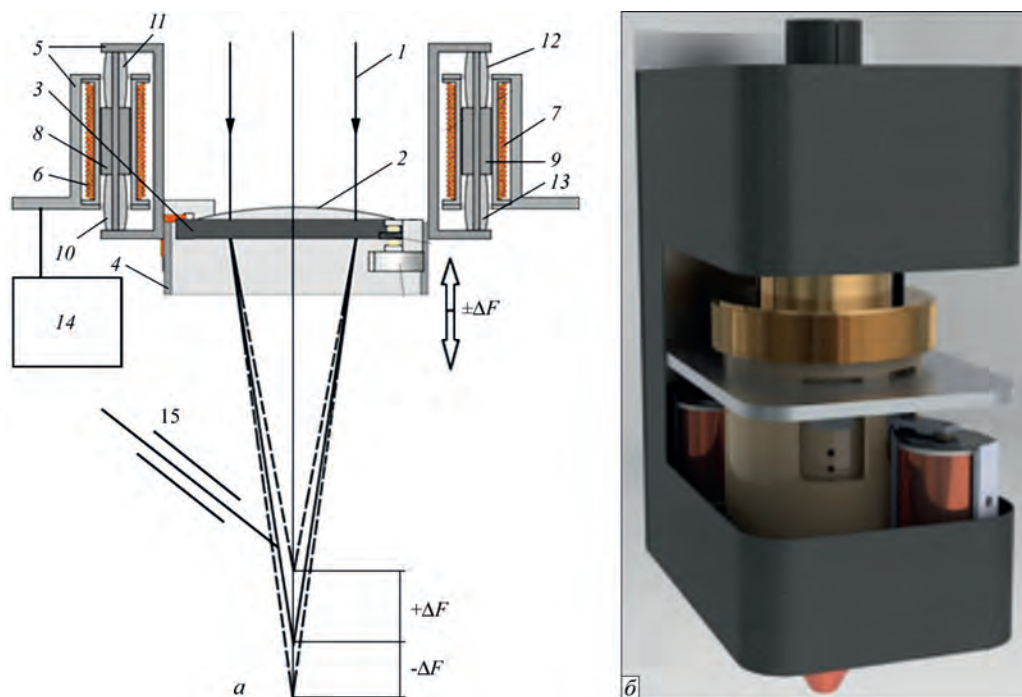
Схема конструкции (а) и общий вид (б) головки для лазерной и гибридной лазер-MIG сварки с системой возвратно-поступательного перемещения (сканирования) фокуса ($\pm\Delta F$) вдоль оси излучения (обозначения см. в тексте)
